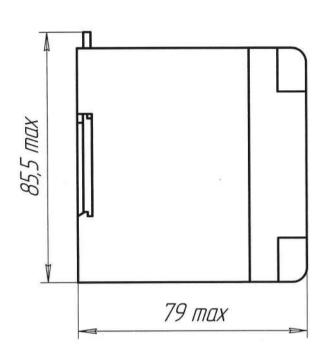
Габаритные, установочные размеры преобразователей переменного тока и напряжения ЕПЗ4Д
